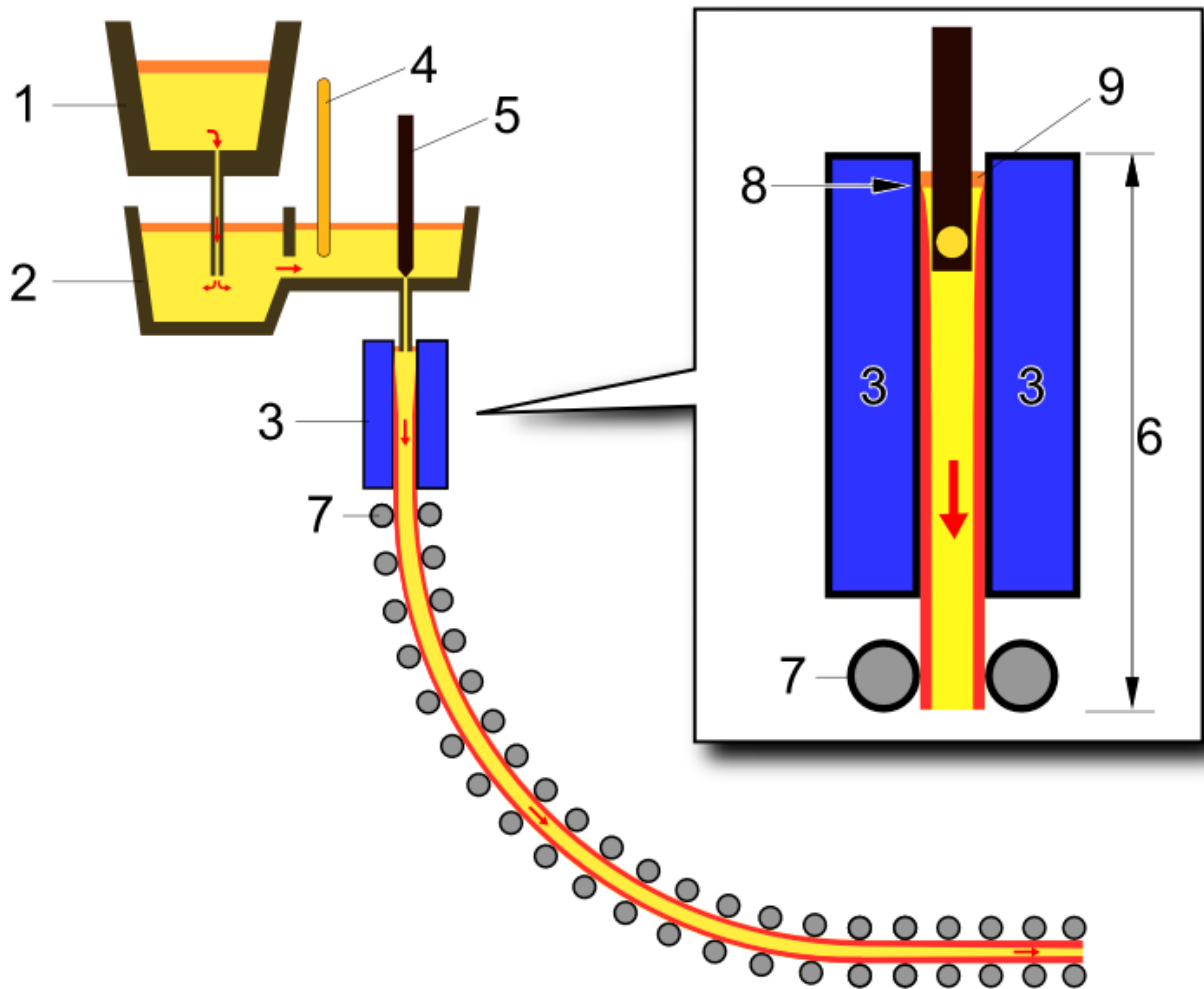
Схема установки непрерывного литья заготовок:
